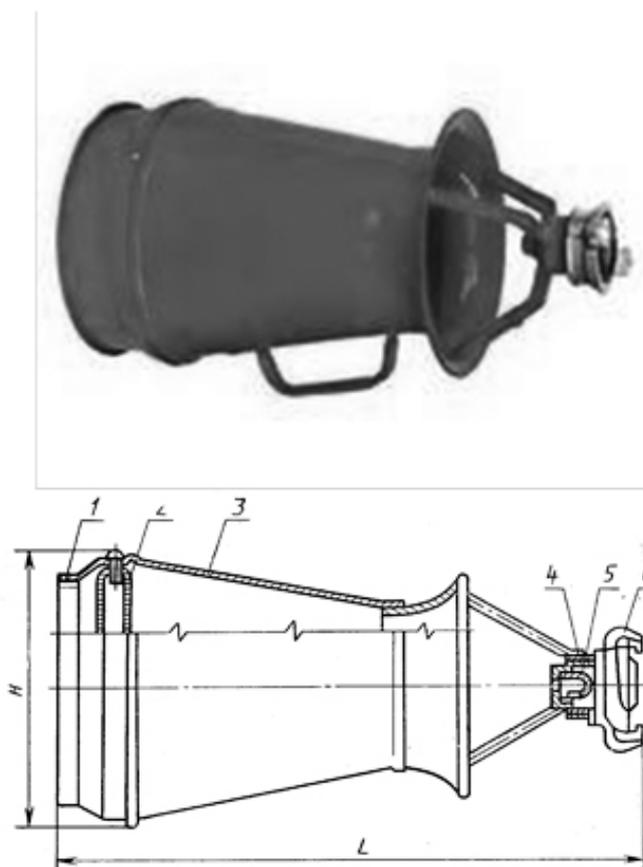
Піногенератор середньої кратності типу ГПС [4]: 1 — насадка, 2 — касета сіток, 3 — корпус генератора; 4 — корпус розпилювача, 5 — розпилювач, 6 — сполучна головка ГМ-50, L — основний габаритний розмір
